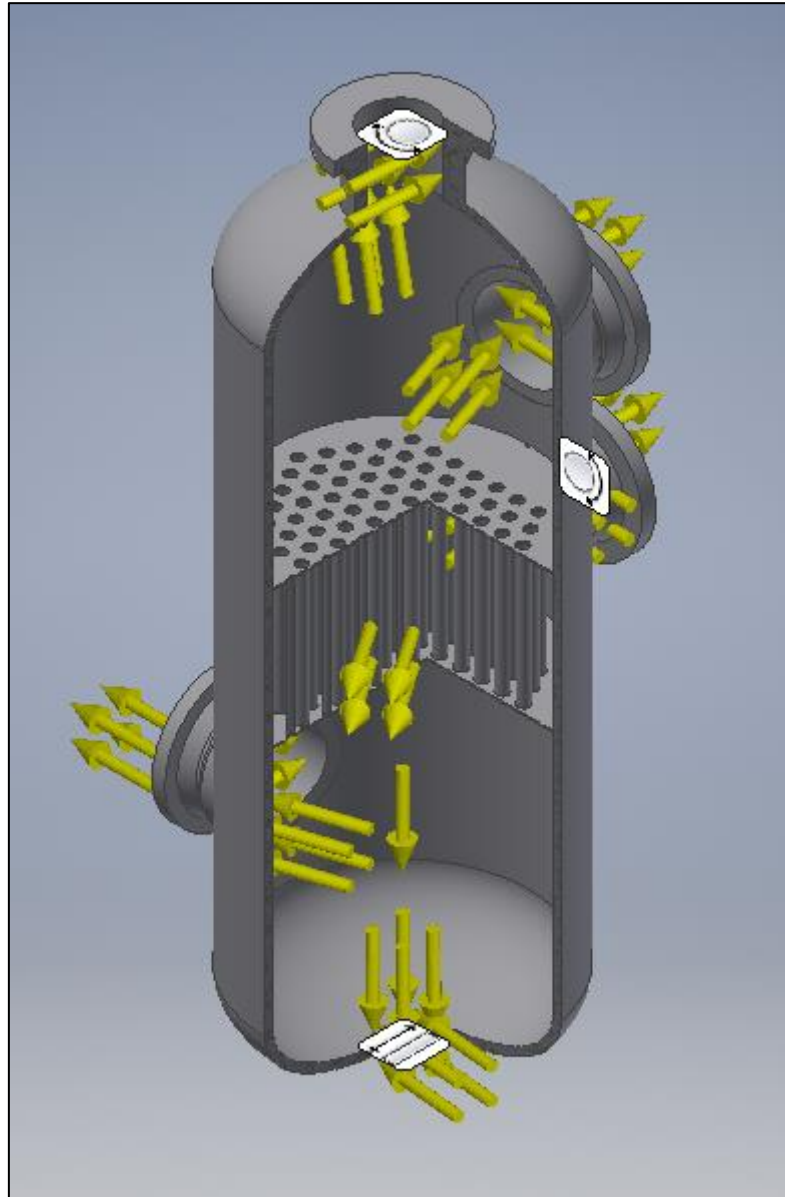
б)–Твердотільна модель корпусу під тиском
